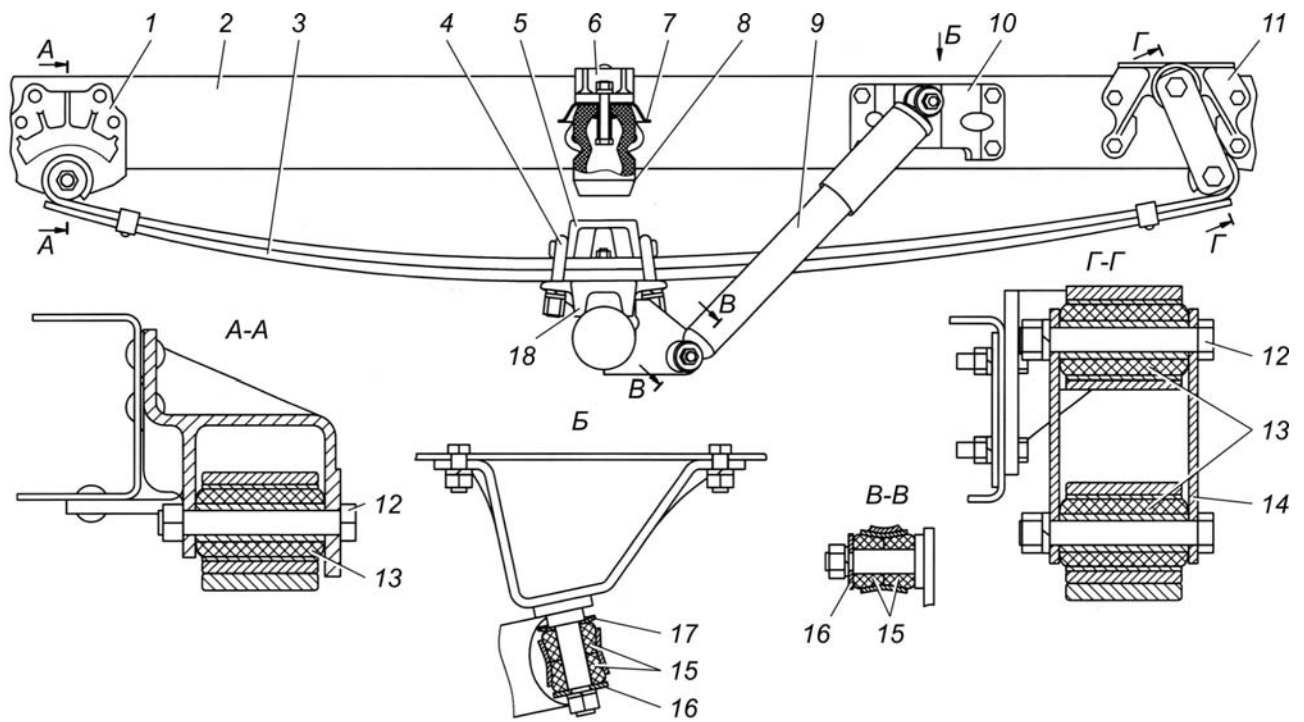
Передняя подвеска автомобилей типа 4x4: 1, 6, 10 и 11 – кронштейны; 2 – лонжерон рамы; 3 – рессора; 4 – стремянка; 5 – накладка; 7 – чашка буфера; 8 – буфер; 9 – амортизатор; 12 – болт; 13 – резинометаллический шарнир; 14 – серьга; 15 – резиновые втулки; 16 и 17 – шайба; 18 – подушка
